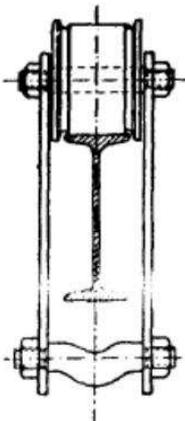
Carro apoyado sobre las alas superiores de una viga para ponerle un tecele de cadena suspendido.
